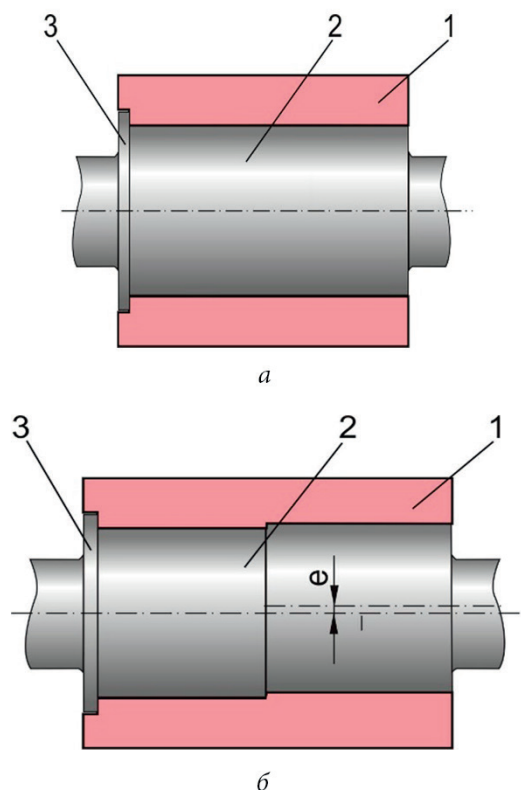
Конструкции соединения несущей оси (приводного вала) со ступицей:
